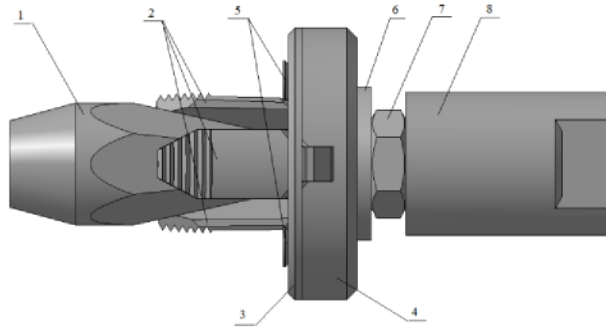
Конструкция узла захвата анкера СЗА: 1 — винт-тяги; 2 — цанги; 3 — кольцо стопорное; 4 — опора; 5 — винты; 6 — шайба; 7 — гайка; 8 — переходная втулка
